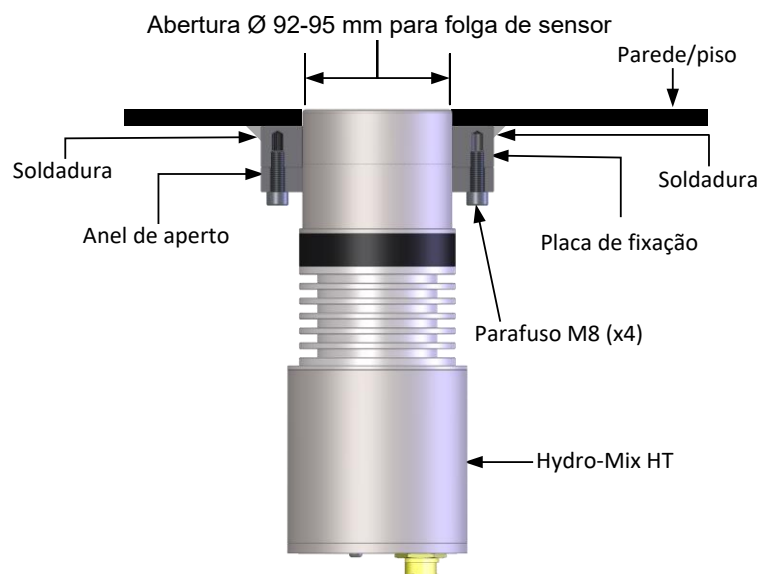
Instalação do sensor (placa de fixação montada externamente)
